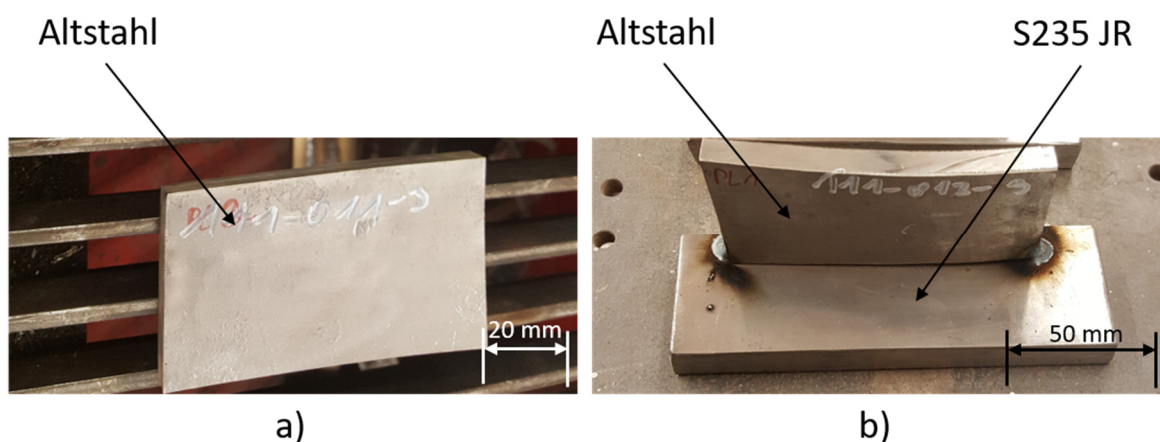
Vorbereitete Schweißversuchsproben a) Auftragsschweißprobe (111-011-3); b) Kehlnahtschweißprobe (111-012-3)
